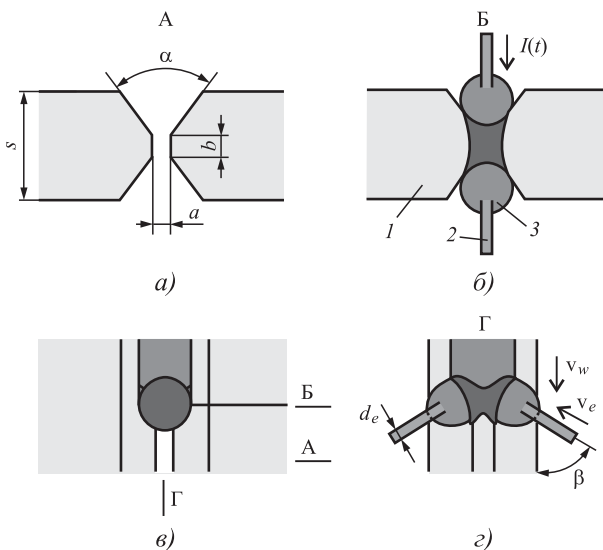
Схема двухдуговой синхронной сварки корня шва вертикального стыка:
